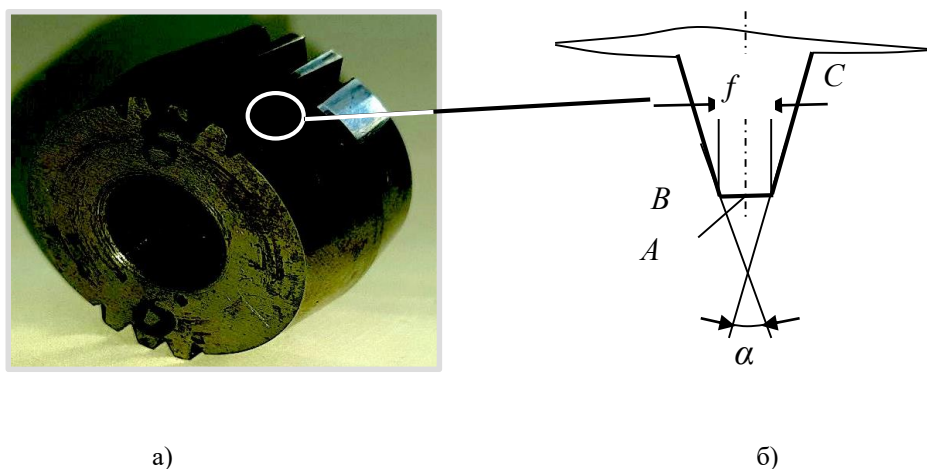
Деформуючий інструмент для формування повздовжніх концентраторів напруг: а) фото інструменту; б) профіль зубця
